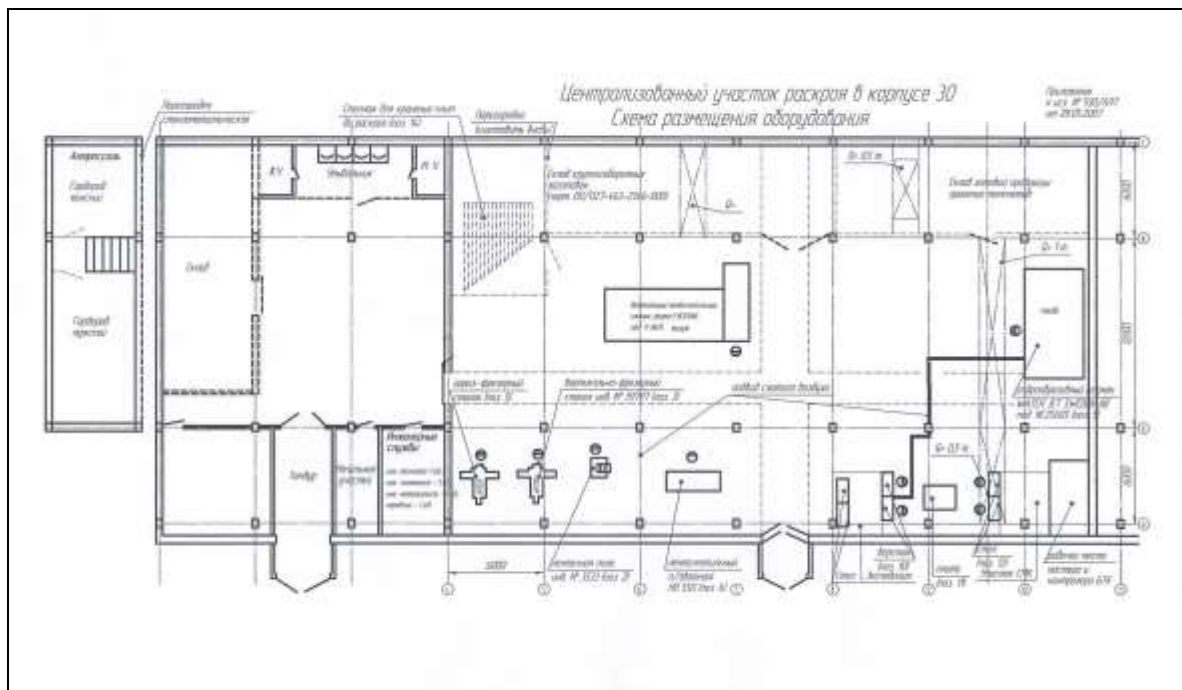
Компоновка участка централизованного раскроя заготовок в корпусе 30
